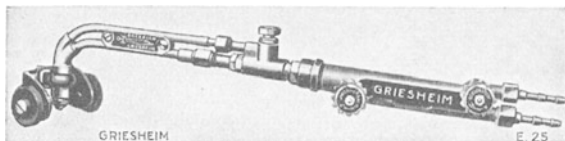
Schneidbrenner, auch für Schweißzwecke geeignet.
